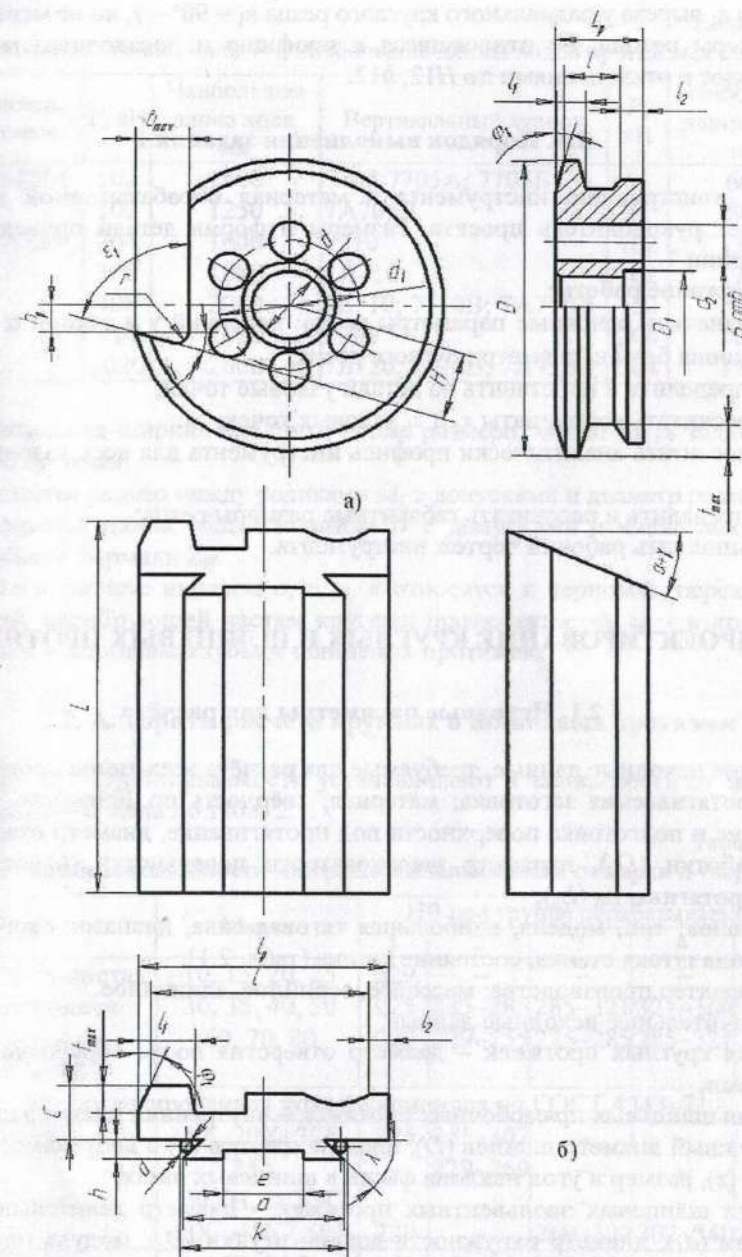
Габаритные и присоединительные размеры радиальных резцов: а – круглый, б – призматический
